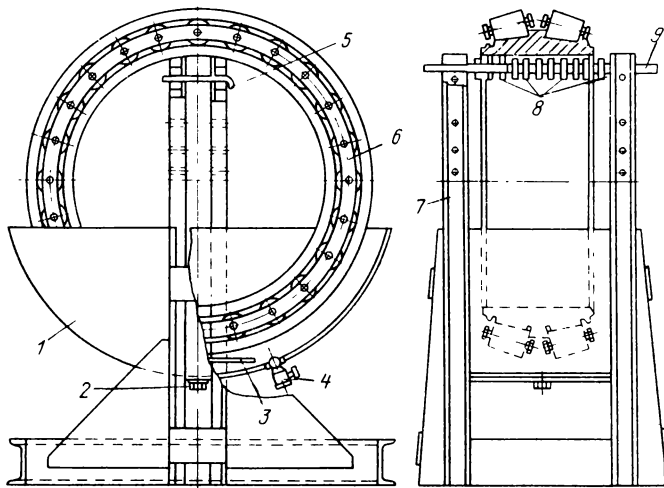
Переносная установка для промывки крупногабаритных подшипников: 1 — ванна; 2 — кран сливной; 3 — решетка; 4 — кран сливной; 5 — ось; 6 — подшипник промываемый; 7 — стойка; 8 — подшипник; 9 — труба
